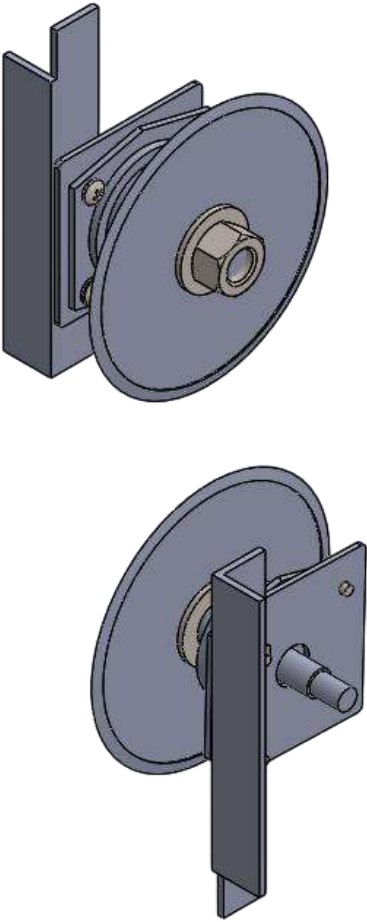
Sistema de corte seleccionado para el desvainado de cacao.
